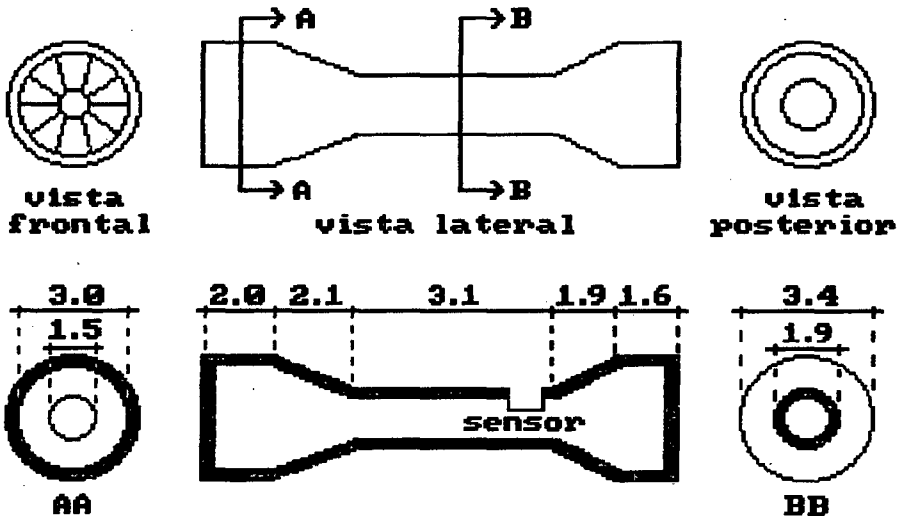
Desenho do transdutor de fluxo. O sentido do fluxo é da esquerda para direita. A turbina fixa localiza-se antes do corte AA (dimensões em cm).
